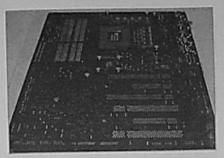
PCB de un motherboard moderno. que puede llegar a tener entre ocho y diez capas intermedias para la interconexión de los componentes soldados a él.
